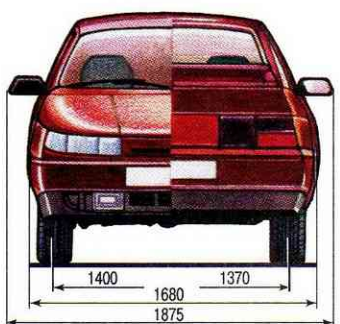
Габаритные размеры автомобиля ВАЗ-2112
